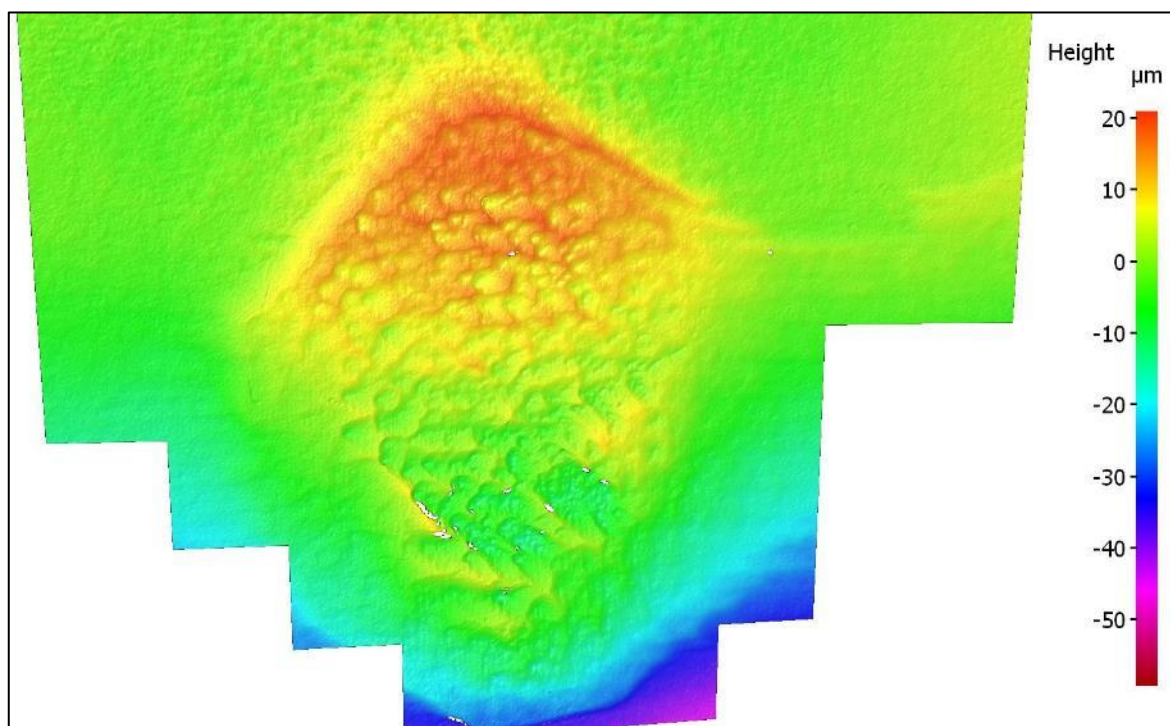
Kontrola 4 – detail spodní části střížné hrany.
